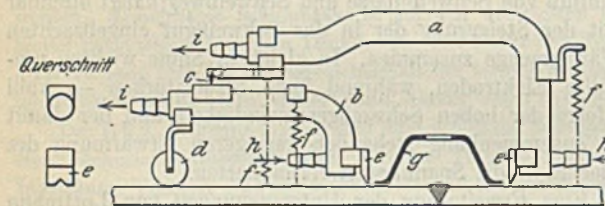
Vollständig gekühltes Spiegelgerät zur Bestimmung der Dehnung in der Schweißnaht.
